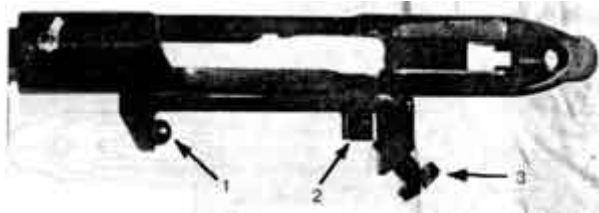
Крепление основания кронштейна на ствольной коробке (вид сверху):
